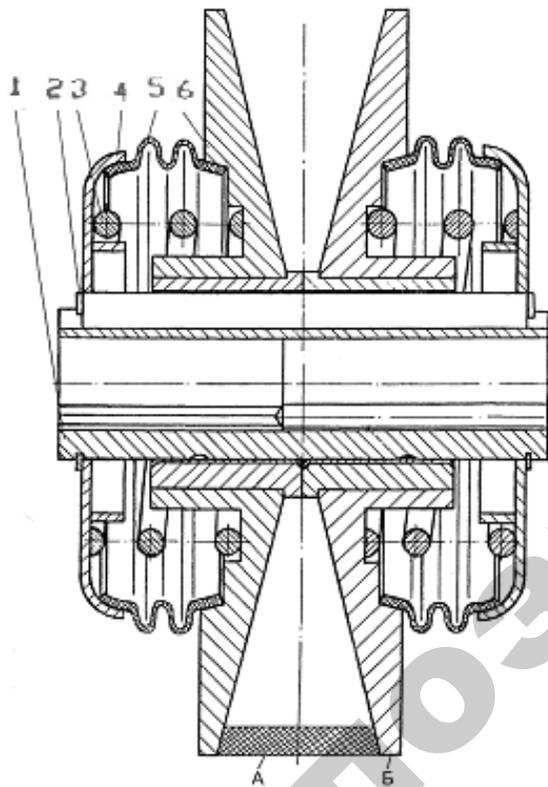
Ведущий шкив вариатора: 1 — вал-втулка; 2 — кольцо; 3 — пружина; 4, 6 — диски; 5 — кожух; А — поверхность ремня; Б — поверхность дисков
